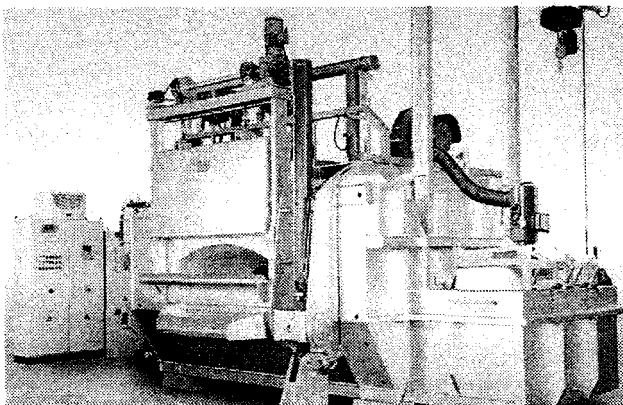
Плавильный газовый комплекс для плавки алюминиевой стружки модели StrikoMelter типа MS/MNS
